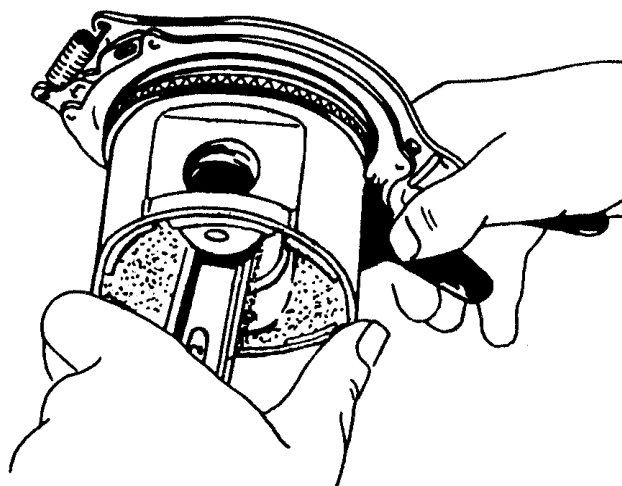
Снятие поршневых колец с поршня приспособлением 5-У-11388
